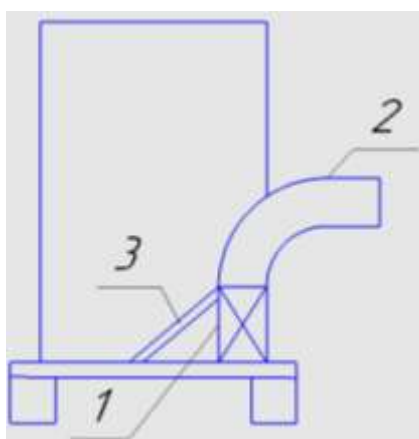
Пневмо-механический высевающий аппарат:1-высевной диск; 2-нагнетательная трубка;3-лапка для крепления трубки
